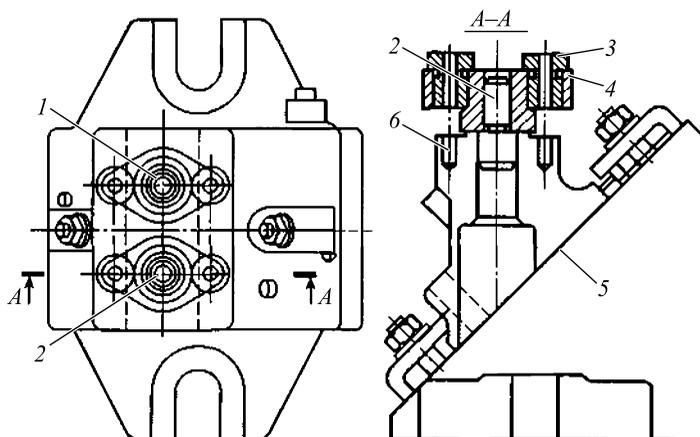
Схема незакрепляемого накладного кондуктора
